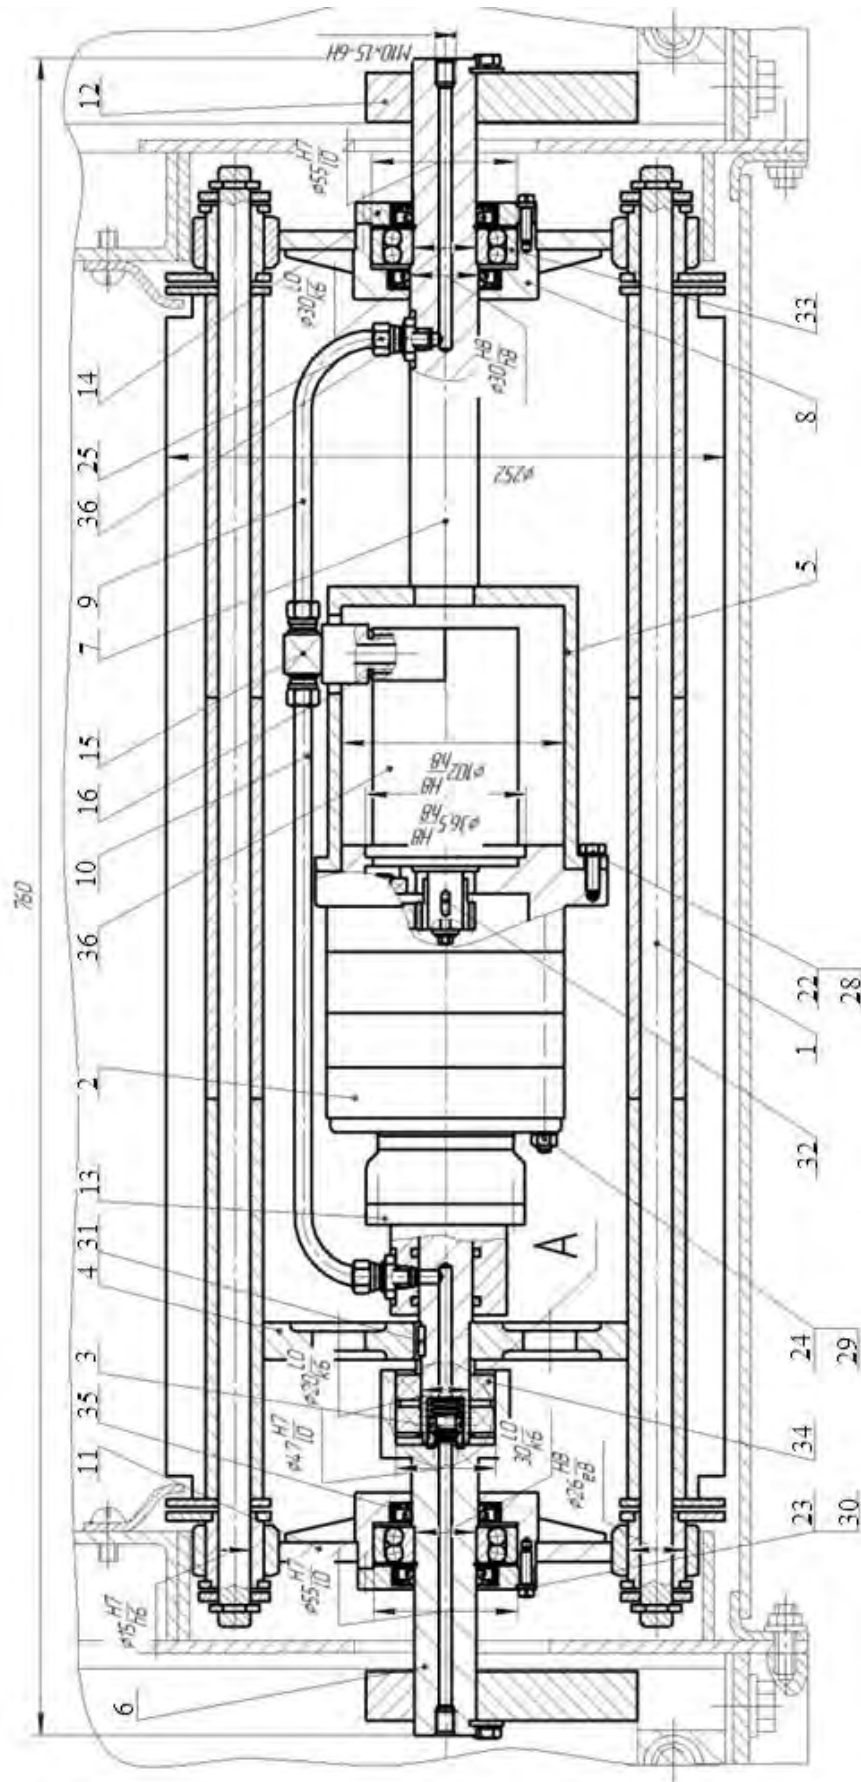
Конструкція вмонтованого приводу скребкового конвеєра для видалення стружки з робочої зони токарного верстата
